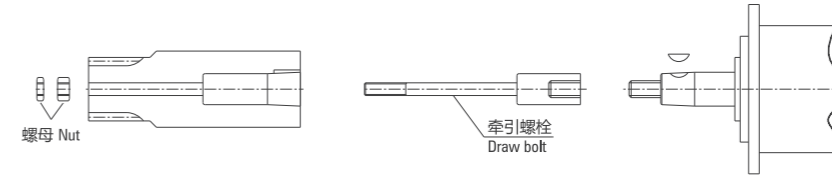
输入齿轮装配 Figure C.5:Input gear assembly
